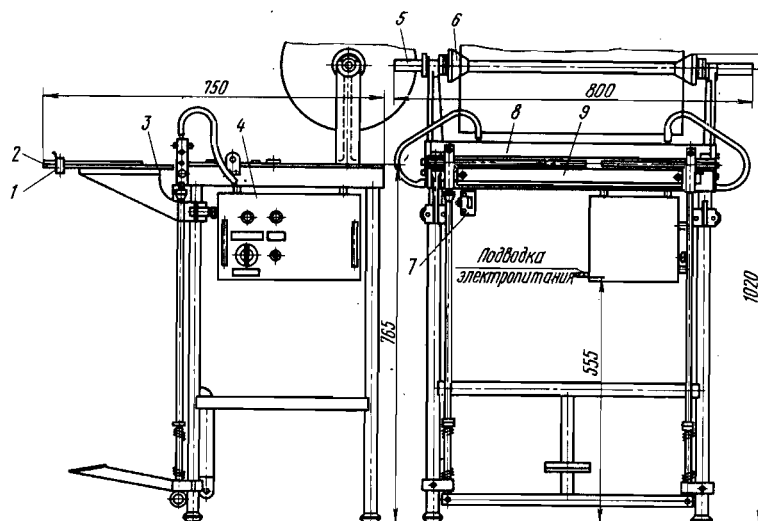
Общий вид машины марки М6-АП-2С для сварки полимерных пленок:
